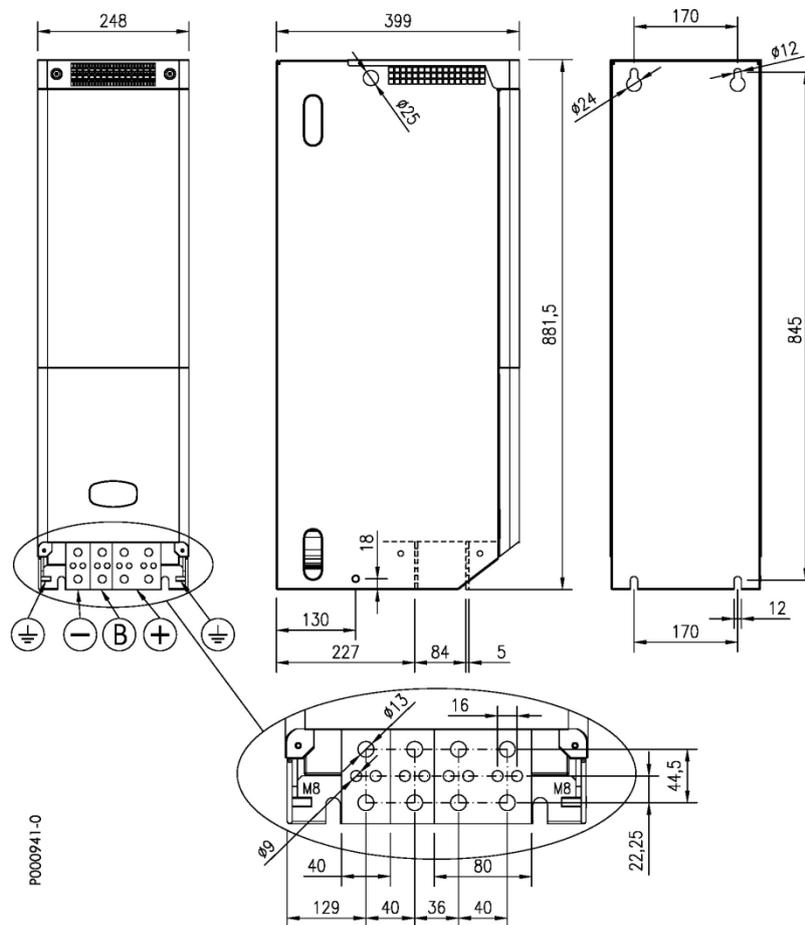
Dimensioni e punti di fissaggio del modulo di frenatura BU600
